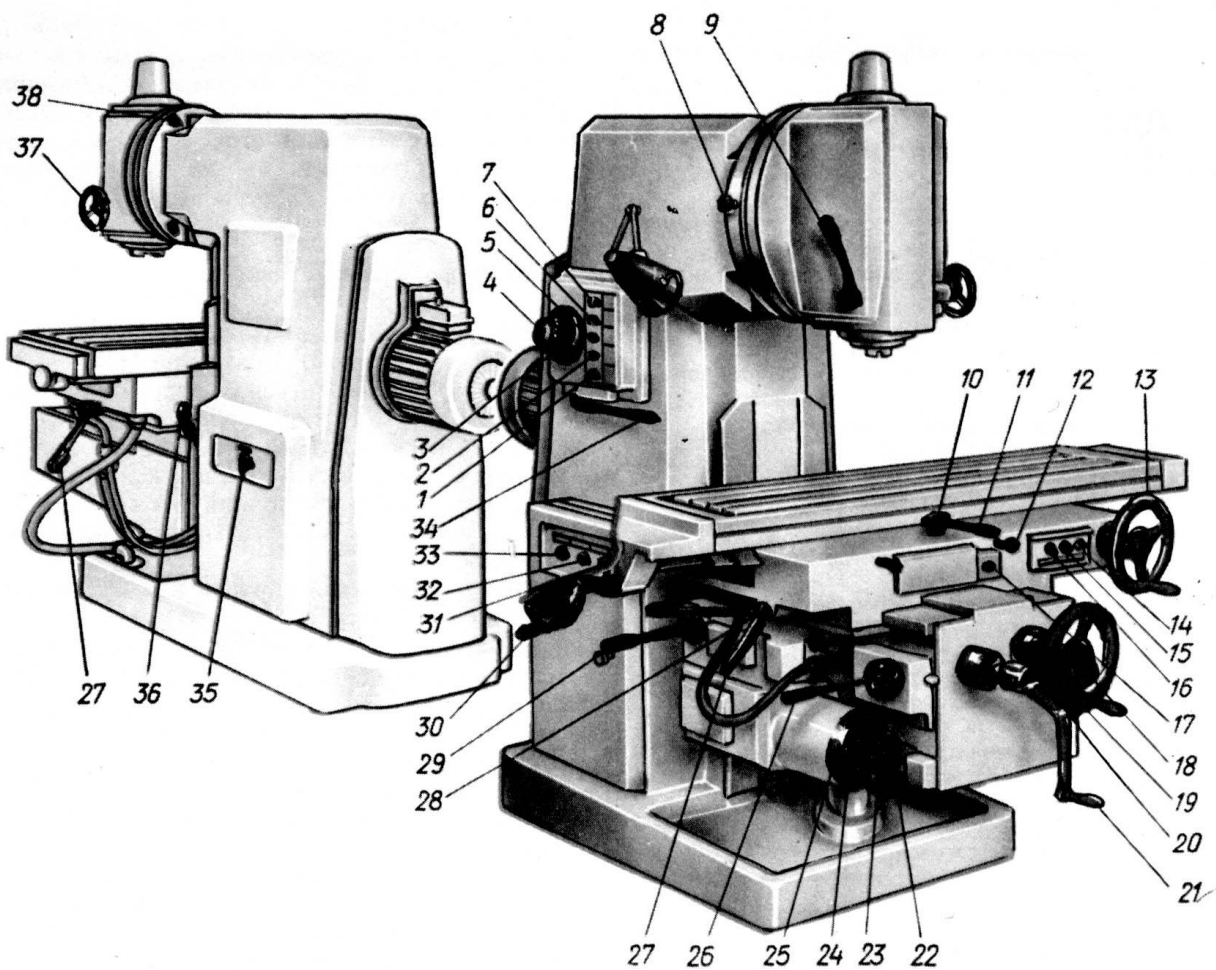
Загальний вид і розміщення органів керування вертикально-фрезерного верстату 6Р-12
